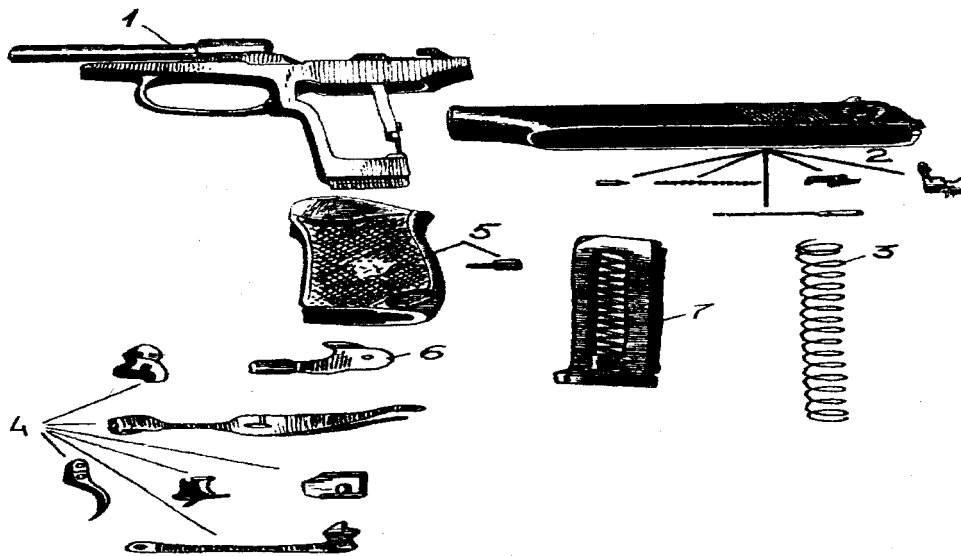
Основні частини та механізми пістолета: 1 - рамка зі стволом, викидачем і запобіжником; 2 - затвор ; 3 - поворотальна пружина; 4 - частина ударно-спускового механізму; 5 - рукоятка з гвинтом; 6 - затворна затримка; 7 - магазин
